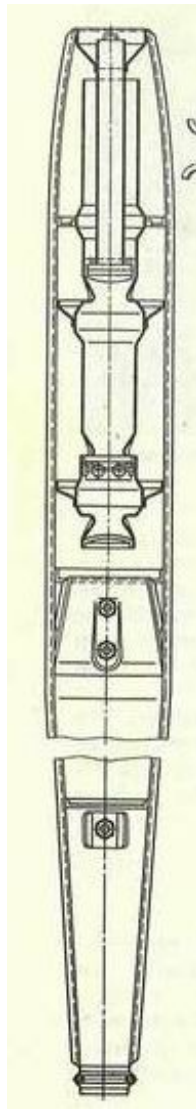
Захват для выемки вставки глушителя шума выпуска
